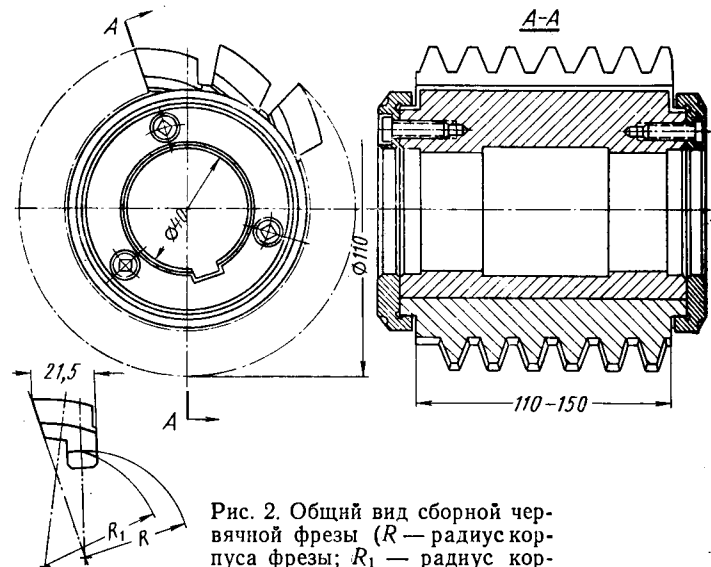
Общий вид сборной червячной фрезы (R — радиус корпуса фрезы; R₁ — радиус корпуса приспособления)
